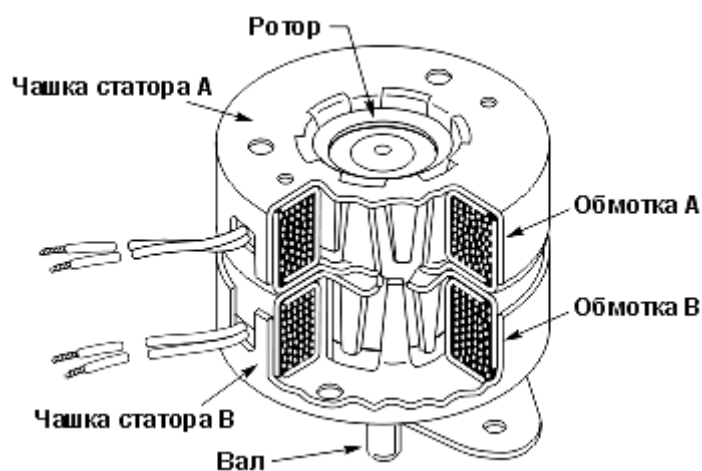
Разрез шагового двигателя с постоянными магнитами
